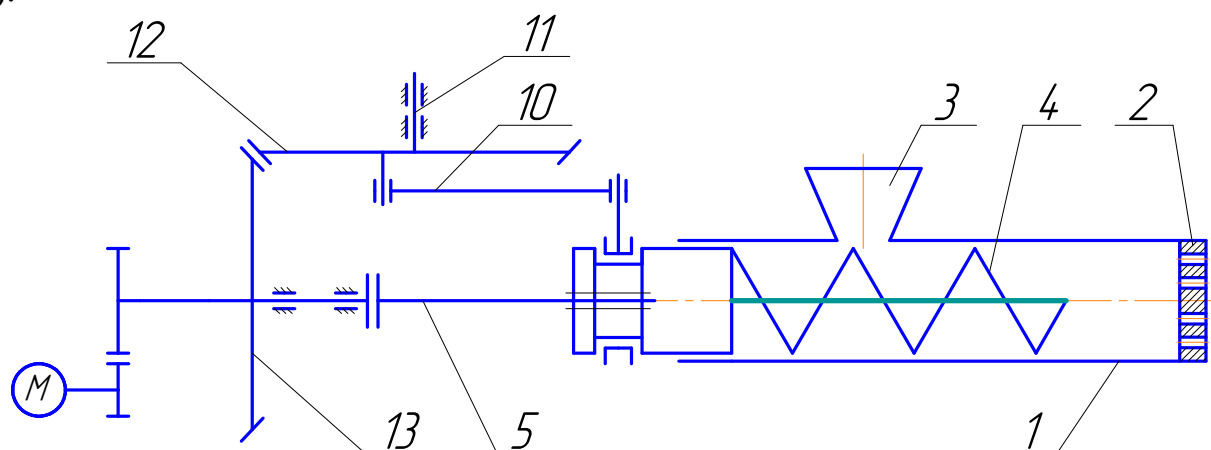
Пресс-экструдер с приводом кривошипа от приводного вала шнека
